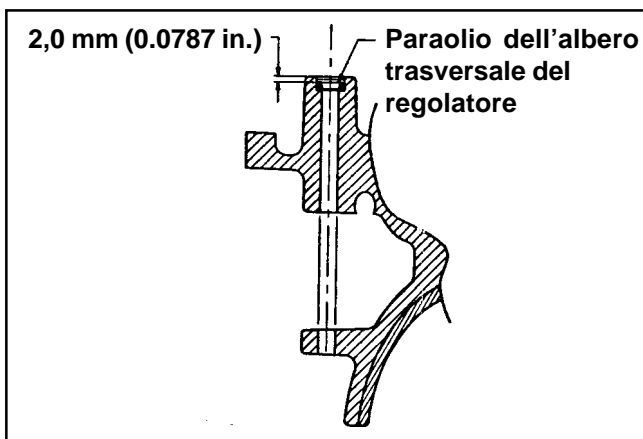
Installazione del paraolio dell'albero trasversale.
